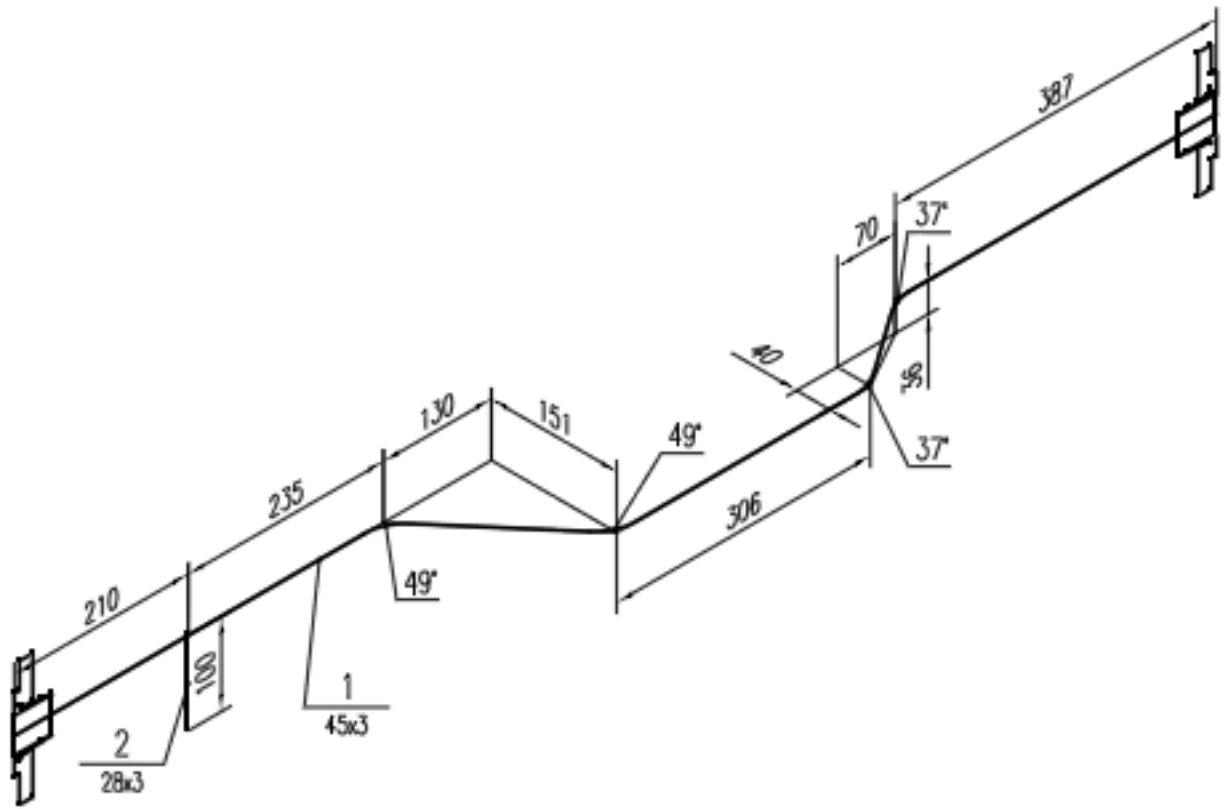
Изометрический чертеж трубы с приварными фланцами
